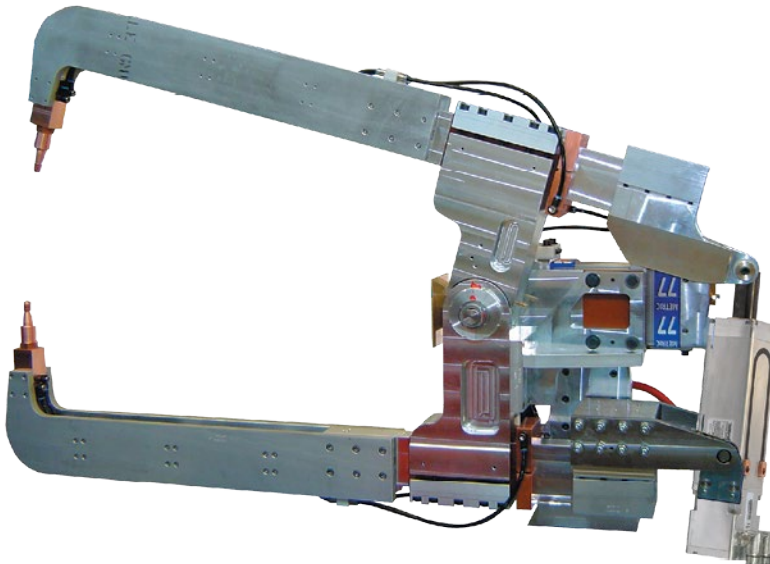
Beispiel eines ServoWeld-Antriebs, der an einer "X"-Schweißzange installiert ist.
